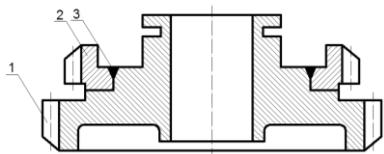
Схема восстановления блока шестерен заменой неисправного зубчатого венца:
